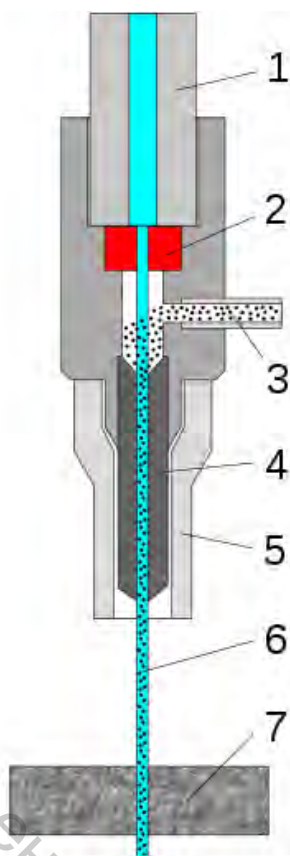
Схема головки установки для гидроабразивных резки материалов:
